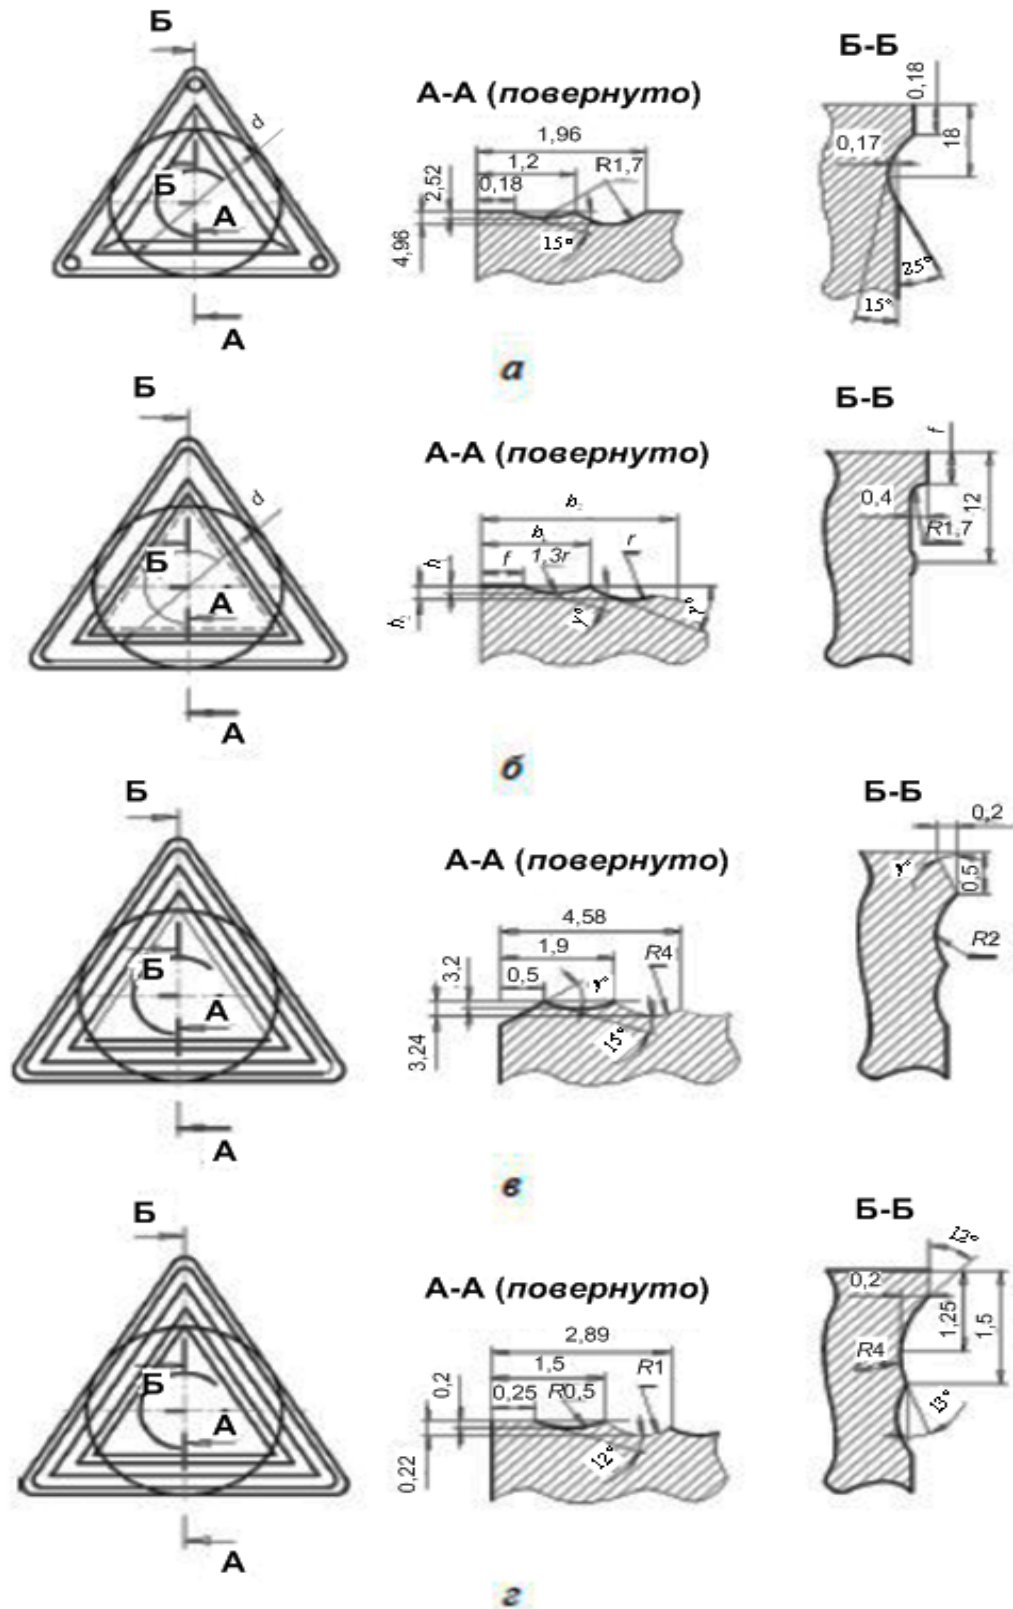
Форми передніх поверхонь ЗПІ:
